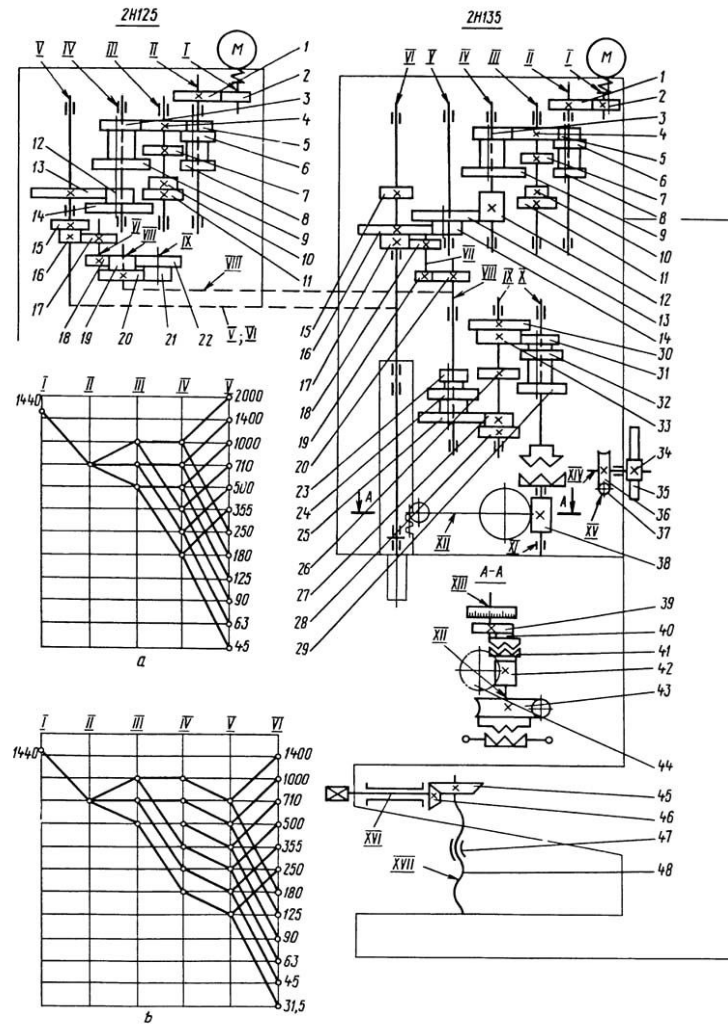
Кінематична схема свердлильного верстата 2H125 (для розміщення в першому розділі)
